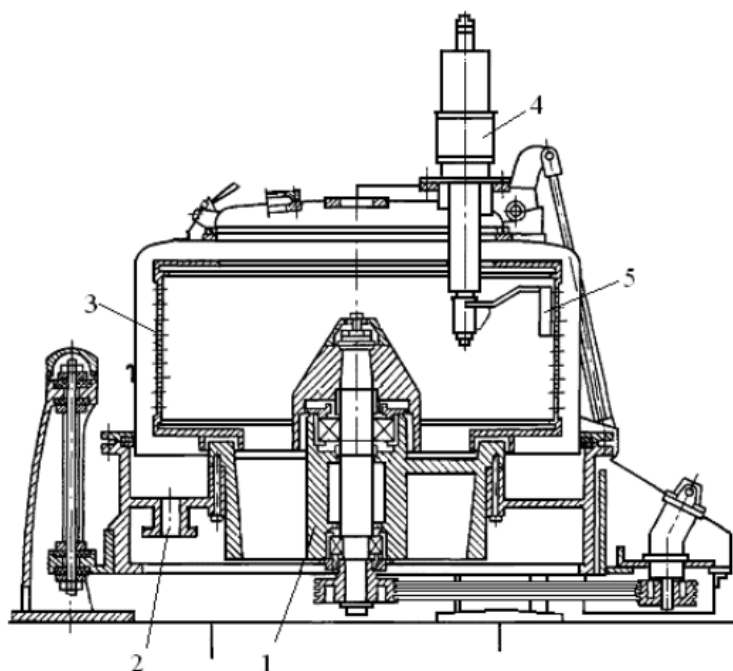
Центрифуга типу ФМН: 1 — корпус приводу; 2 — штуцер; 3 — ротор; 4 — механізм зрізання осаду; 5 — ніж
